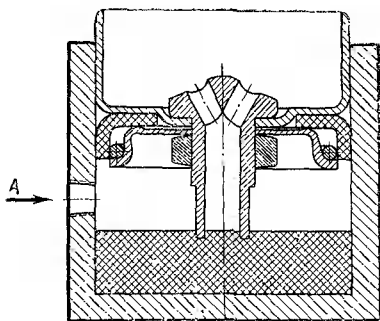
Схема испытания поршня тормозного крана на герметичность:
